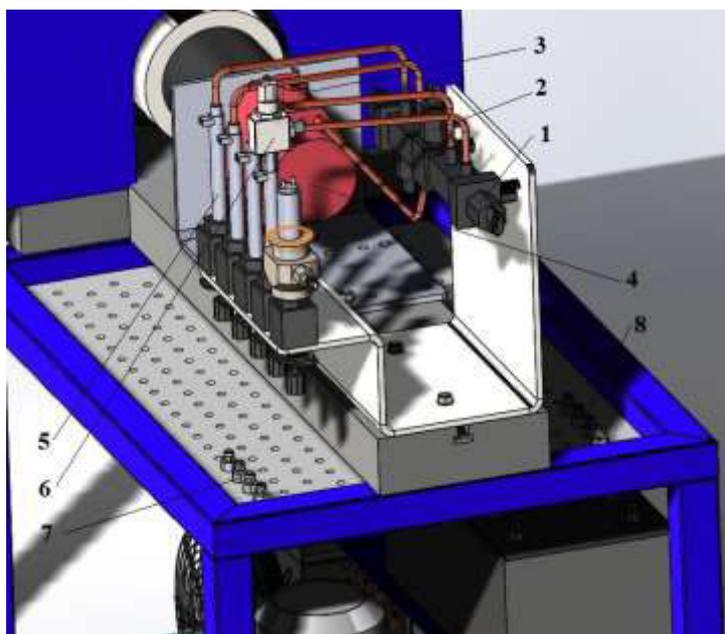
Модернизированный стенд ДД 10-01 (рабочая зона)
